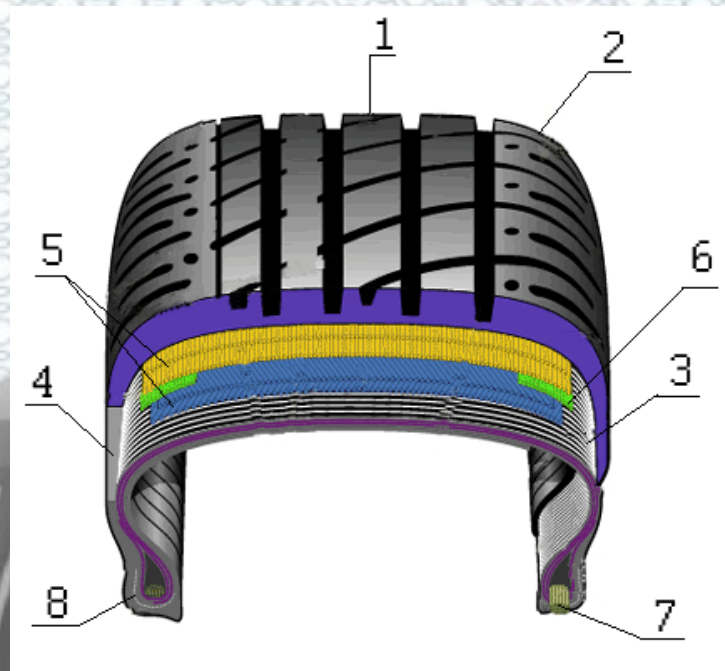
Конструкція пневматичної шини: 1 — протектор; 2 — плечовий блок з ламелями; 3 — каркас; 4 — боковина; 5 і 6 — брекер; 7 — бортове кільце; 8 — борт шини
